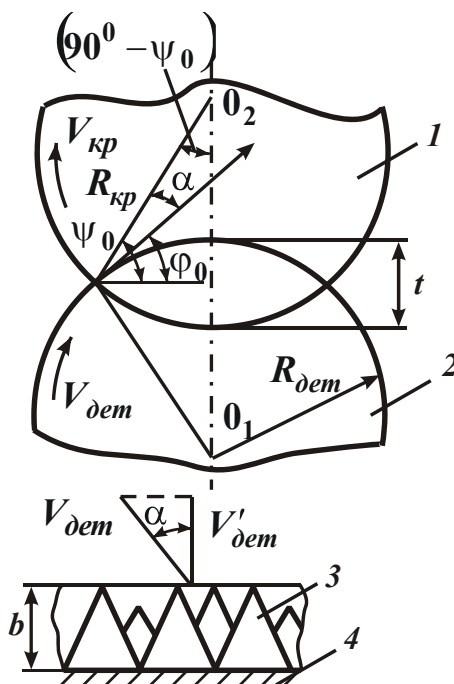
Расчетная схема круглого продольного шлифования:
